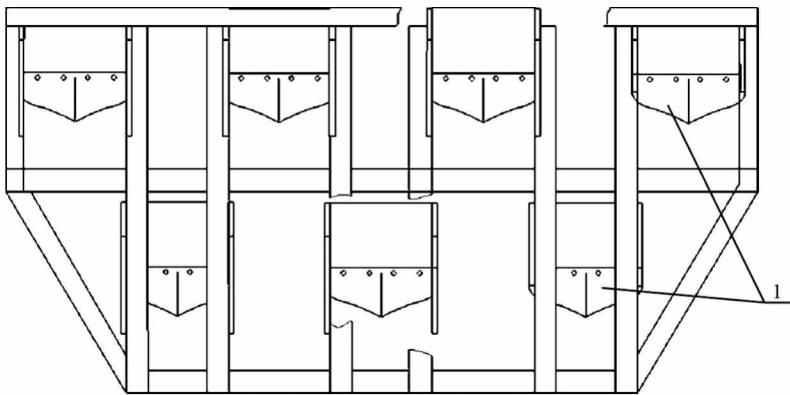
Схема устройства для создания полосы противопожарного назначения (вид сверху): 1 – культиваторные лапы в два ряда
